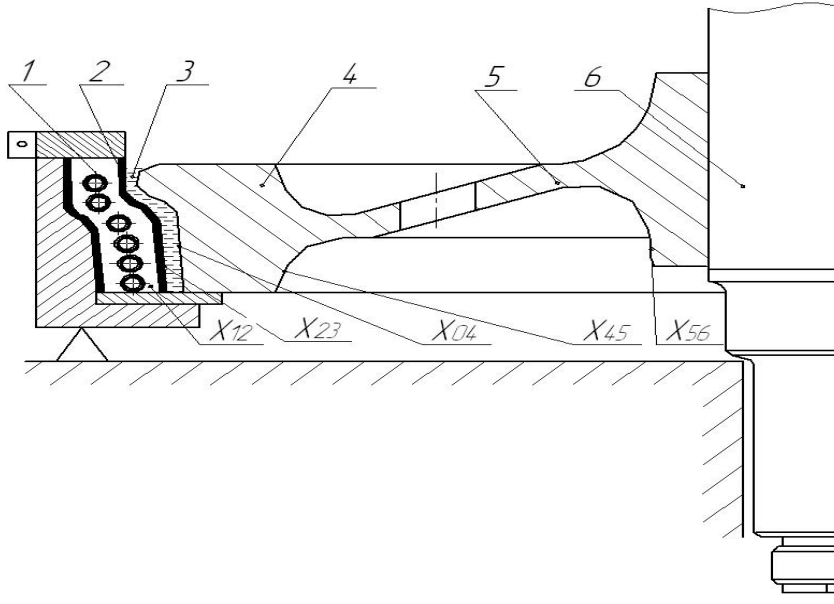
Розрахункова схема 1 – багатовитковий кільцевий індуктор; 2 – вогнетривка ізоляція тигля; 3 – розплавлений метал, тигель; 4 – деталь (обод); 5 – однодисковий центр; 6 – вісь спарованого металевого колеса; x_{12} – зона між індуктором та ізоляцією; x_{23} – зона між ізоляцією та розплавленим металом; x_{04} – зона між розплавленим металом та зношеною поверхнею металевого колеса; x_{45} – зона між ободом центра та ступецею центра; x_{56} – зона між ступицею центра та віссю колеса
